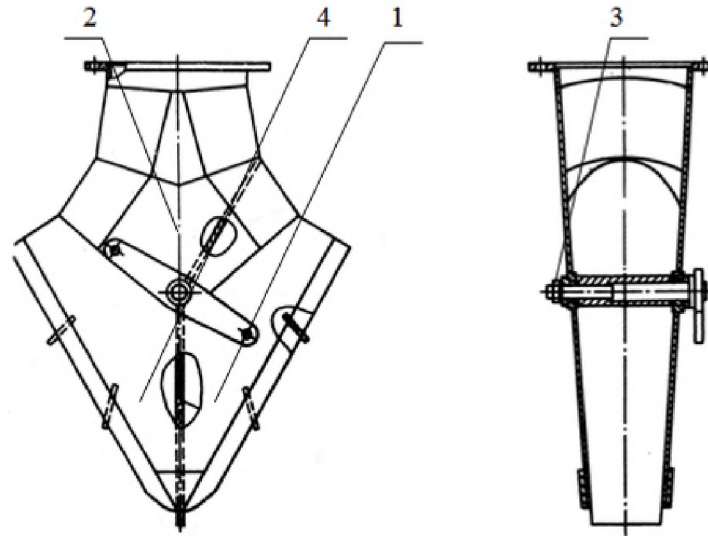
Механічний забірний пристрій: 1 – корпус; 2 – поворотна заслінка; 3 – важіль керування заслінкою; 4 – перегородка.
